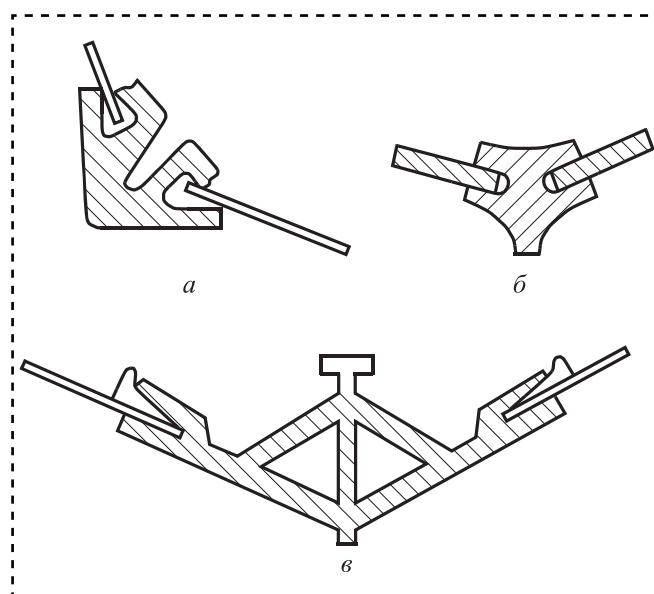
Конструкции корпуса малых катеров с гофрированными элементами жесткости:
